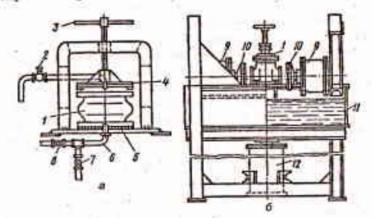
Приспособление (a) и ванна (б) для испытания арматуры:
